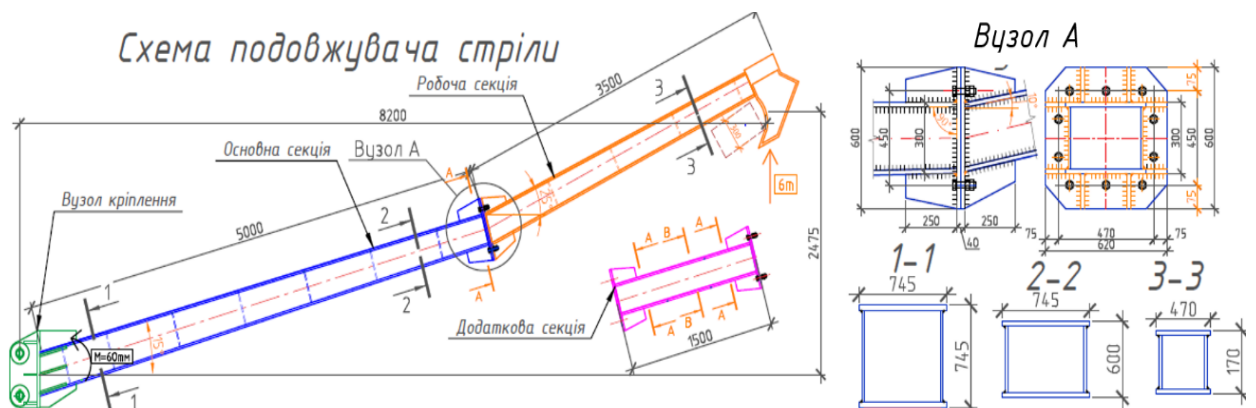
Конструкційна схема подовжувача стріли екскаватору
